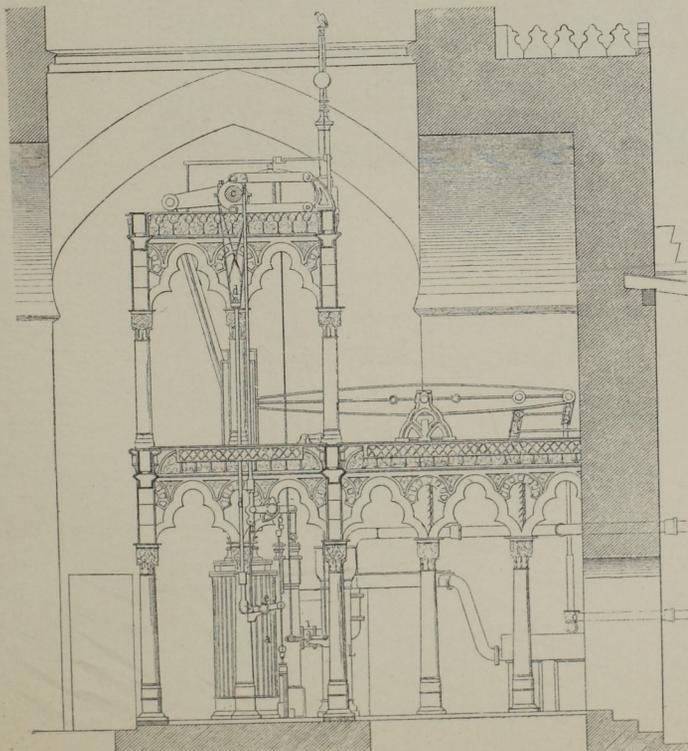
Seitenansicht der Maschinen. Masst. 1 : 90.
